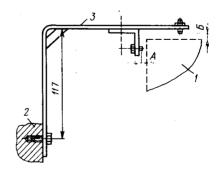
Приспособление для проверки соосности валов с эластичной муфтой:
